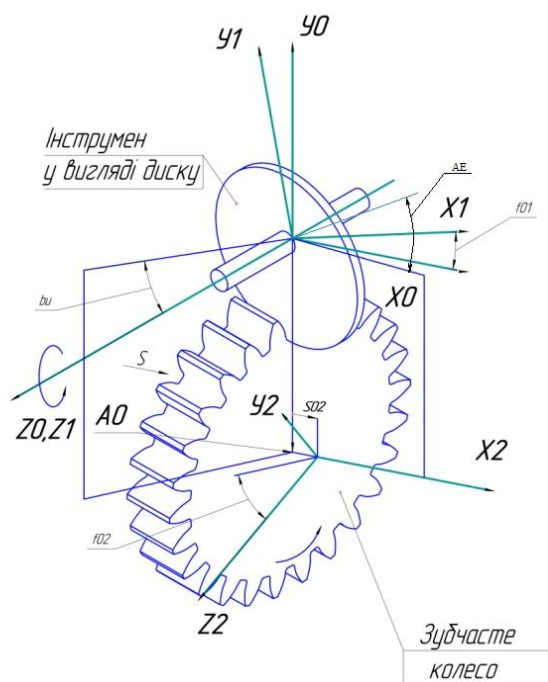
Розрахункова схема формоутворення циліндричних зубчастих коліс дисковим інструментом
